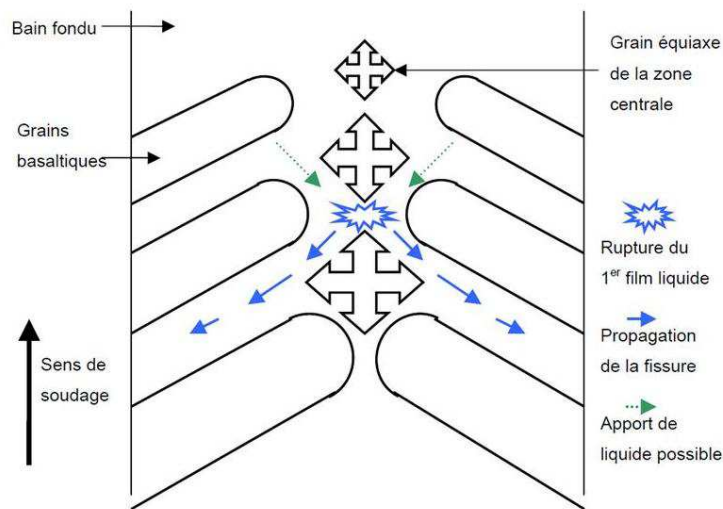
Scénario de fissuration à chaud en soudage laser [27]
